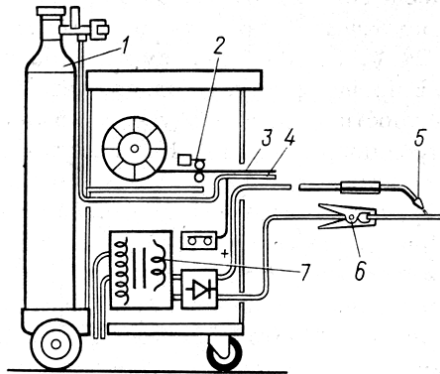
Упрощенная схема сварочного полуавтомата:
